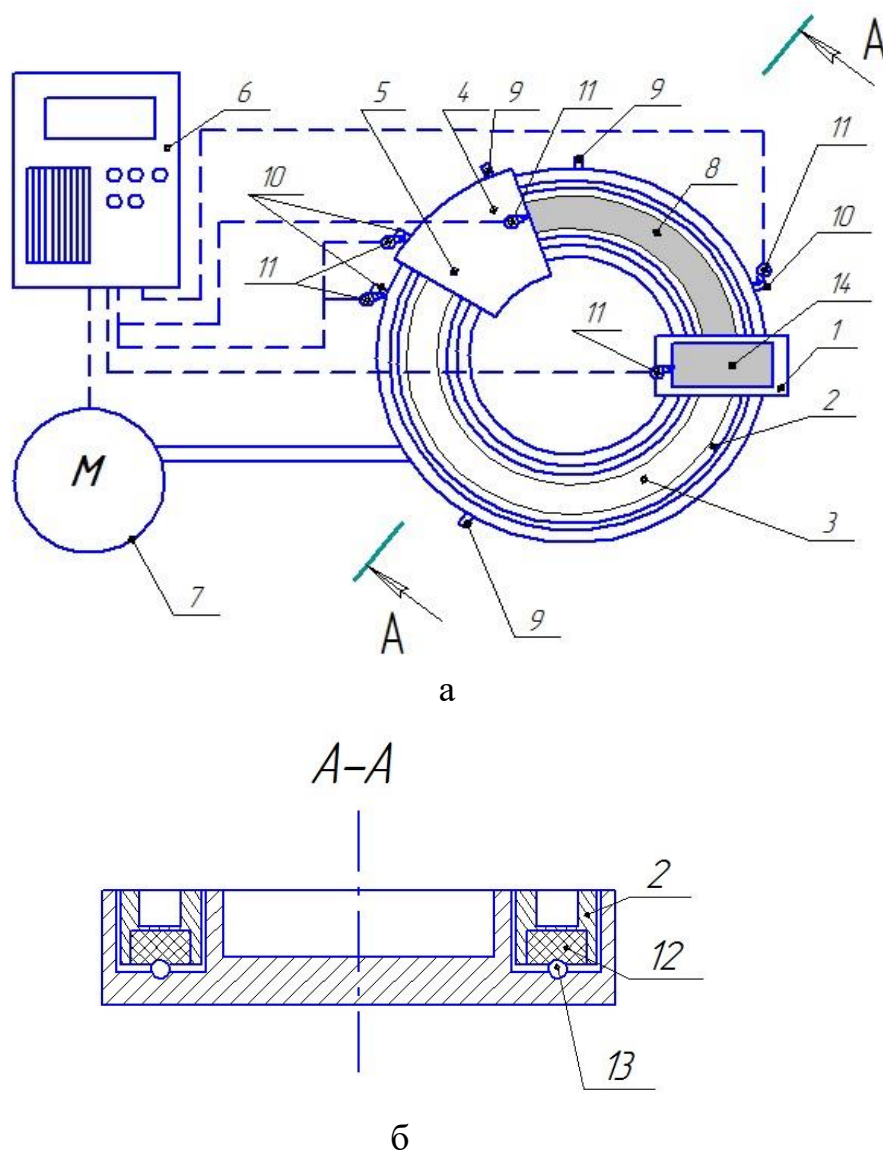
Схема установки терморегулирования для непрерывного литья и прессования цветных металлов и сплавов: а – общий вид; б – сечение установки
